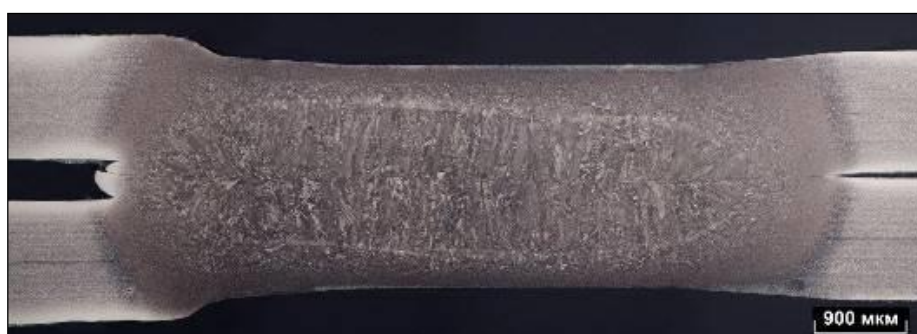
Макроструктура сварной точки 1.1.1
